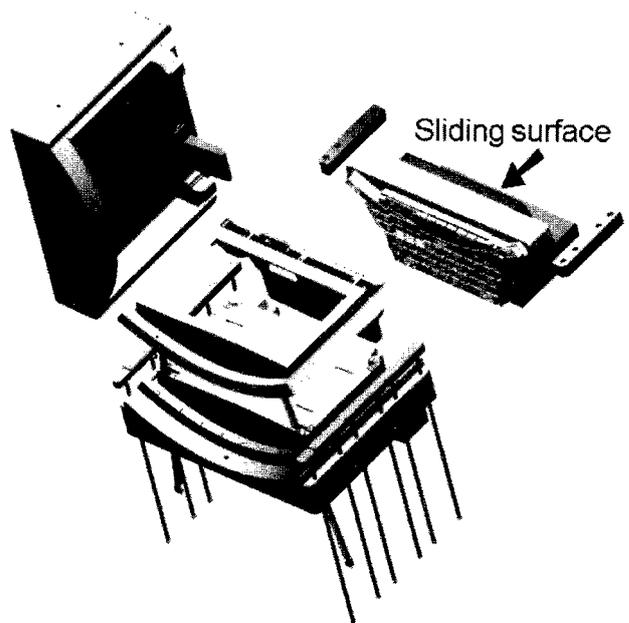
Imold for SolidWorks에 의하여 생성된 금형의 코어, 캐비티, 슬라이드 코어. 가운데에 흐린 색으로 보이는 것이 원래의 플라스틱 제품
